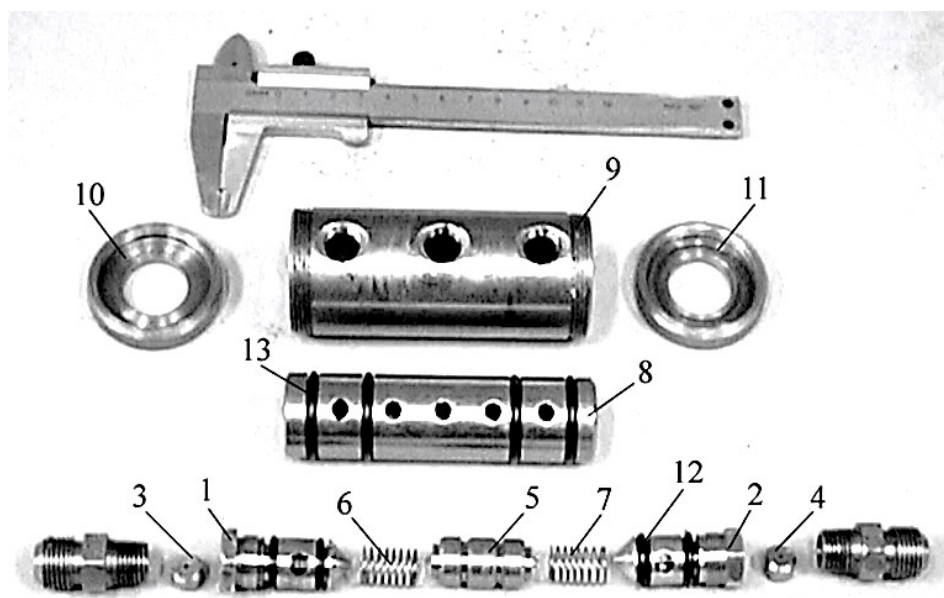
Детали опытного образца инерционного измерительного преобразователя с элементами сопло-заслонка: 1, 2 – сопла; 3, 4 – постоянные дроссели; 5 – инерционная заслонка; 6, 7 – пружины; 8 – гильза; 9 – корпус; 10, 11 – крышки; 12, 13 – уплотнения /
